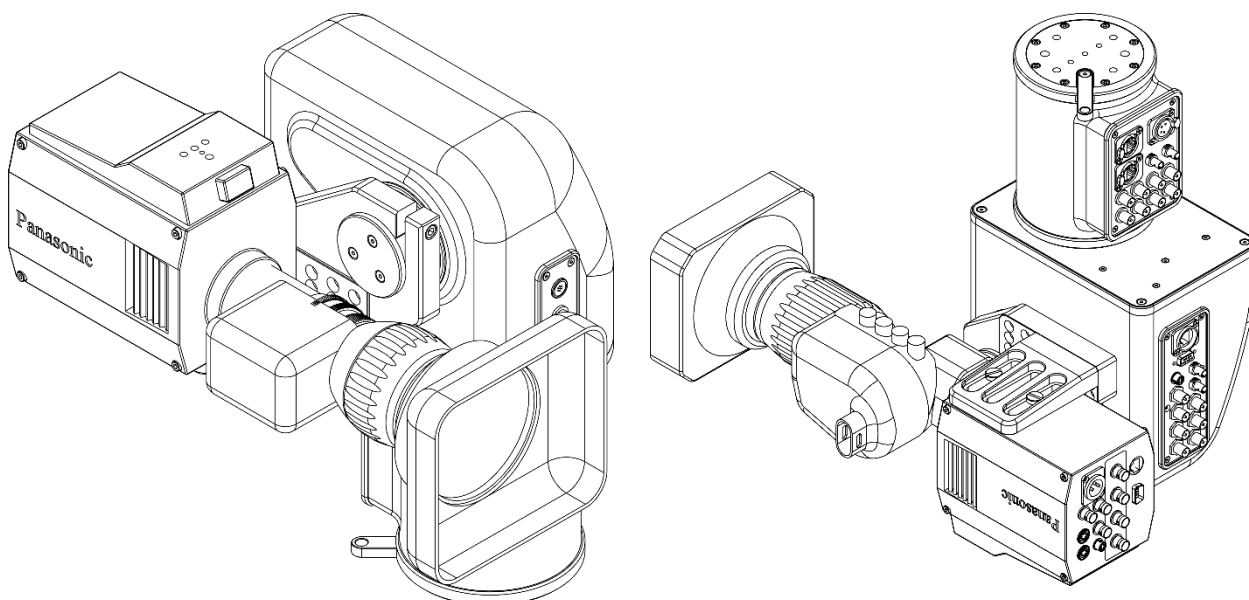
Монтаж боксовой камеры на «стандартное» крепление камеры
